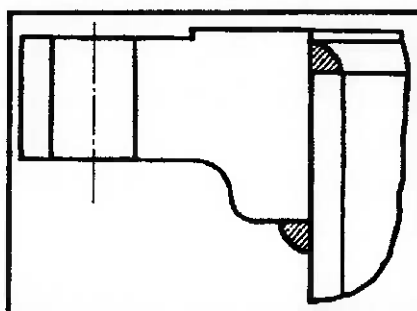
Soldagem do flange ao pescoço da Boca de Visita
